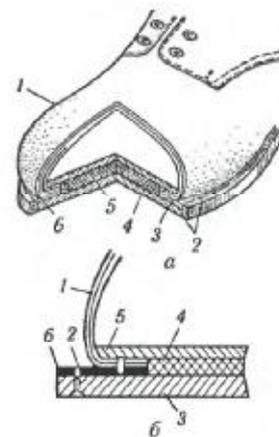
Кріплення методом парко: *a* — розріз взуття; *b* — схема кріплення; 1 — заготівка; 2 — ниткові шви; 3 — підшва; 4 — простинка; 5 — устілка; 6 — рант
